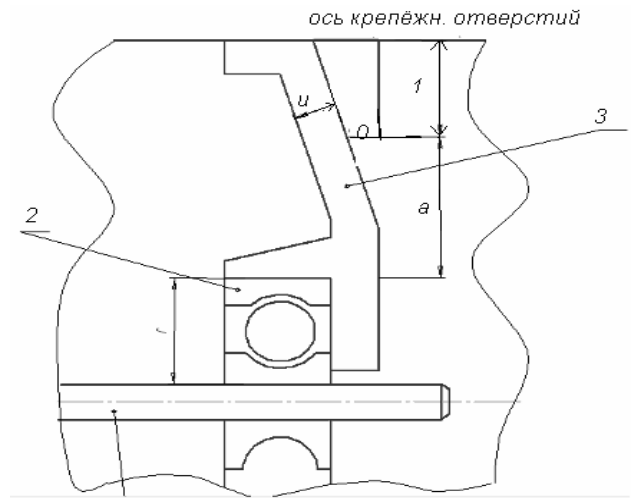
Схема приведения сил: 1 – вал, 2 – подшипник, 3 – подшипниковый щит
